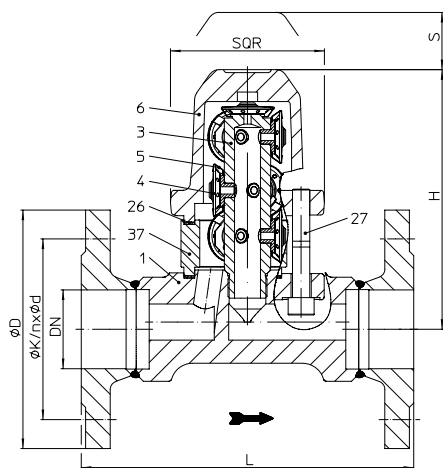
1....10K2 (DN40-50) com 10 cápsulas, com flanges
